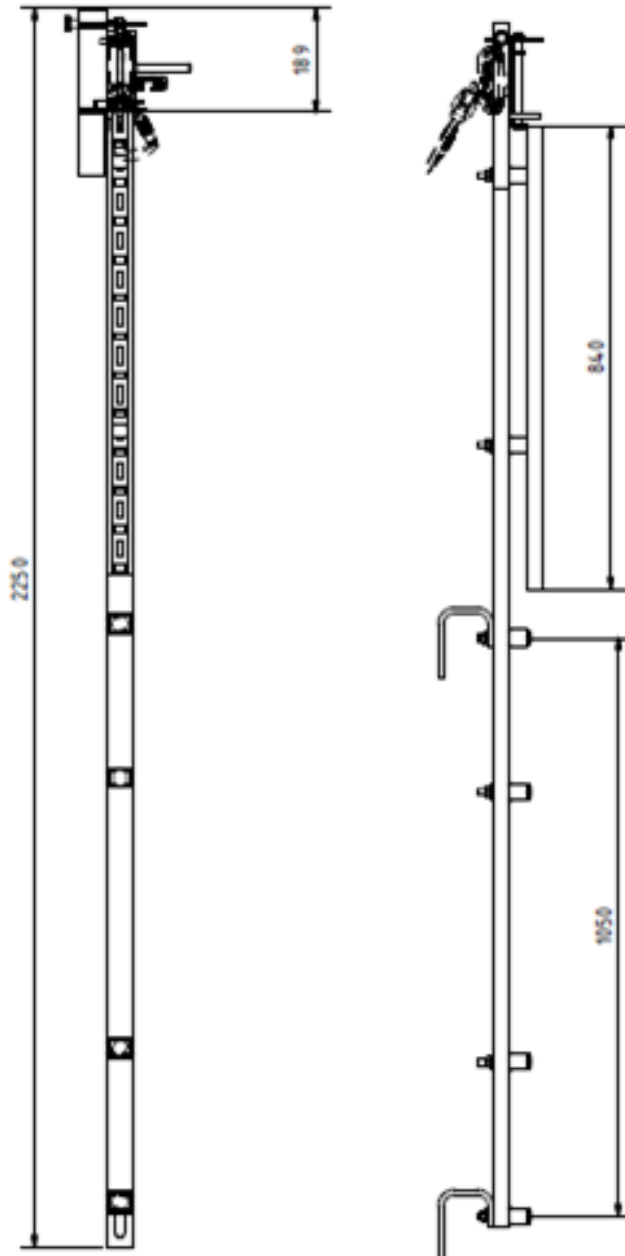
Holmverstärkungselemente mit Dachausstieg
